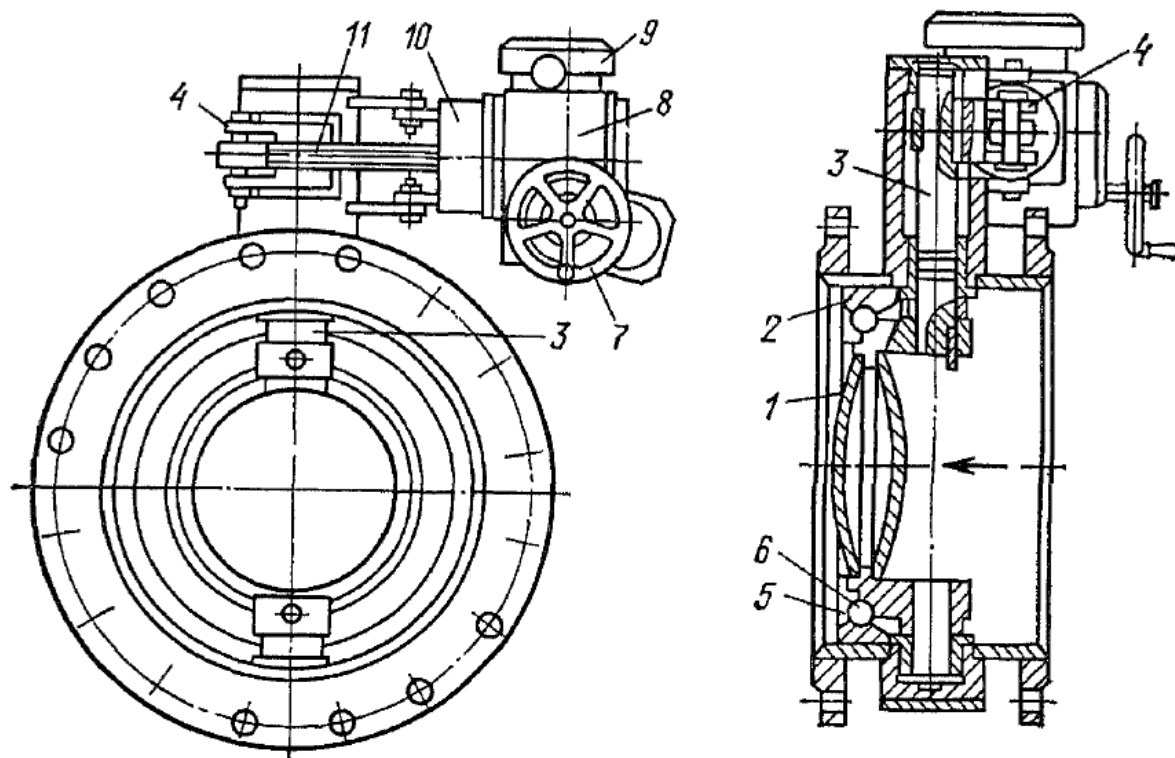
Затвор поворотный дисковый на давление $p_y = 1$ МПа
